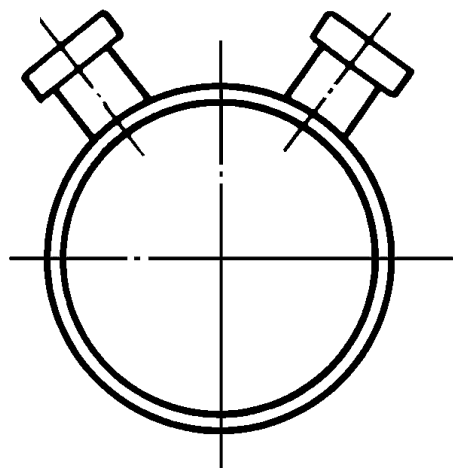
Блок электронагревательный резервуарный БЭР-12
